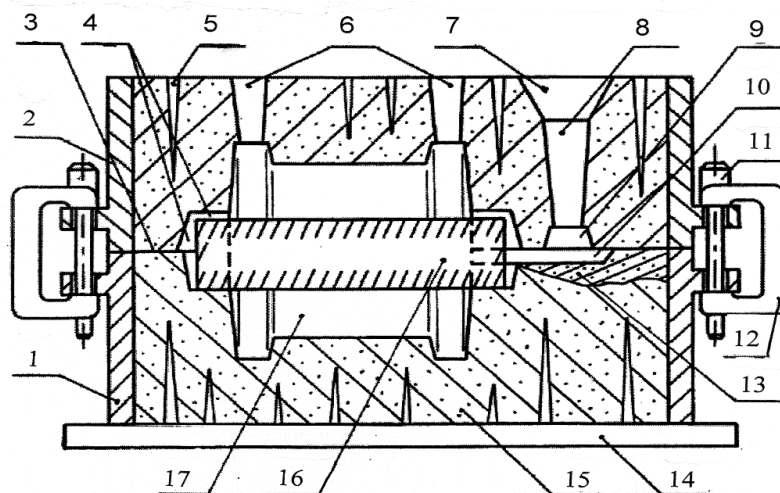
Эскиз песчаной литейной формы в сборе: 1 – нижняя опока; 2 – верхняя опока; 3 – плоскость разъёма; 4 – зазоры; 5 – вентиляционный канал; 6 – выпоры; 7 – литниковая воронка; 8 – стояк; 9 – шлакоуловитель; 10 – питатель; 11 – центрирующий штырь; 12 – скоба; 13 – местный разрез; 14 – плита; 15 – формовочная смесь; 16 – стержень; 17 – рабочая полость формы
